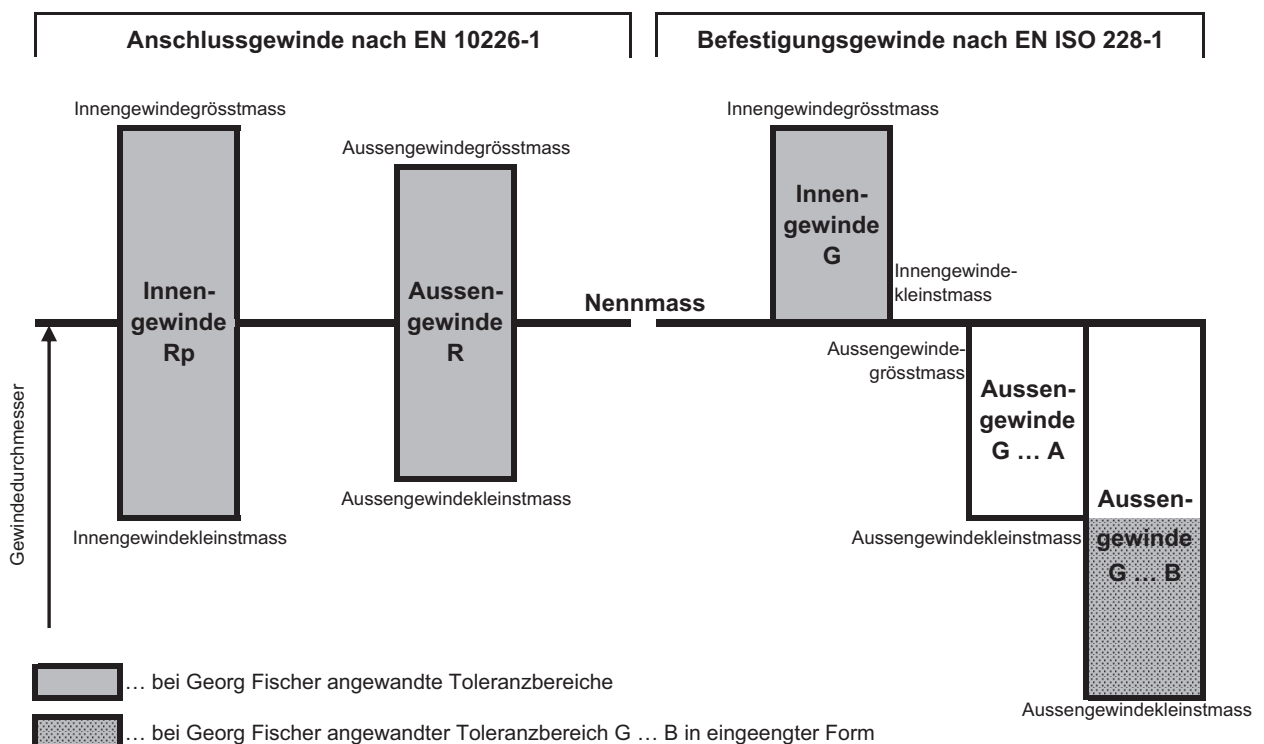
Toleranzlagen von Anschluss- und Befestigungsgewinden
